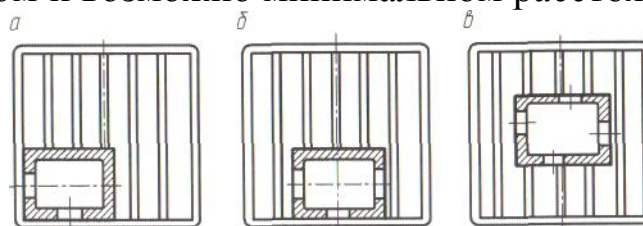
Схема расположения заготовки при обработке: а – с двух сторон; б – с трех сторон; в – с четырех сторон
